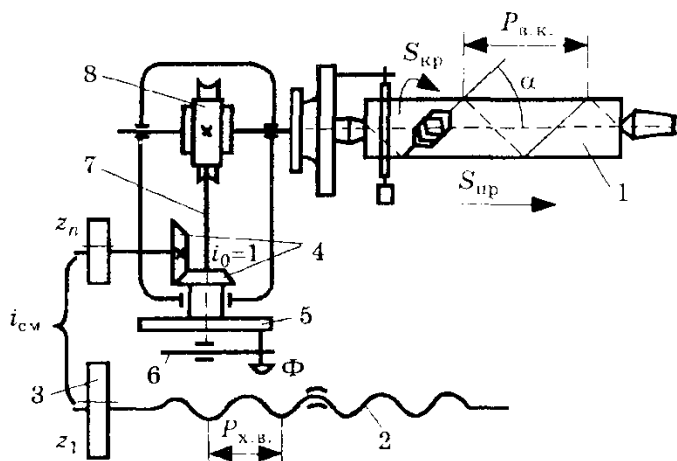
Кинематическая схема головки при фрезеровании винтовых канавок
